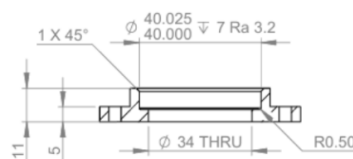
Engineering Drawing: AMT Encoder Mounting
